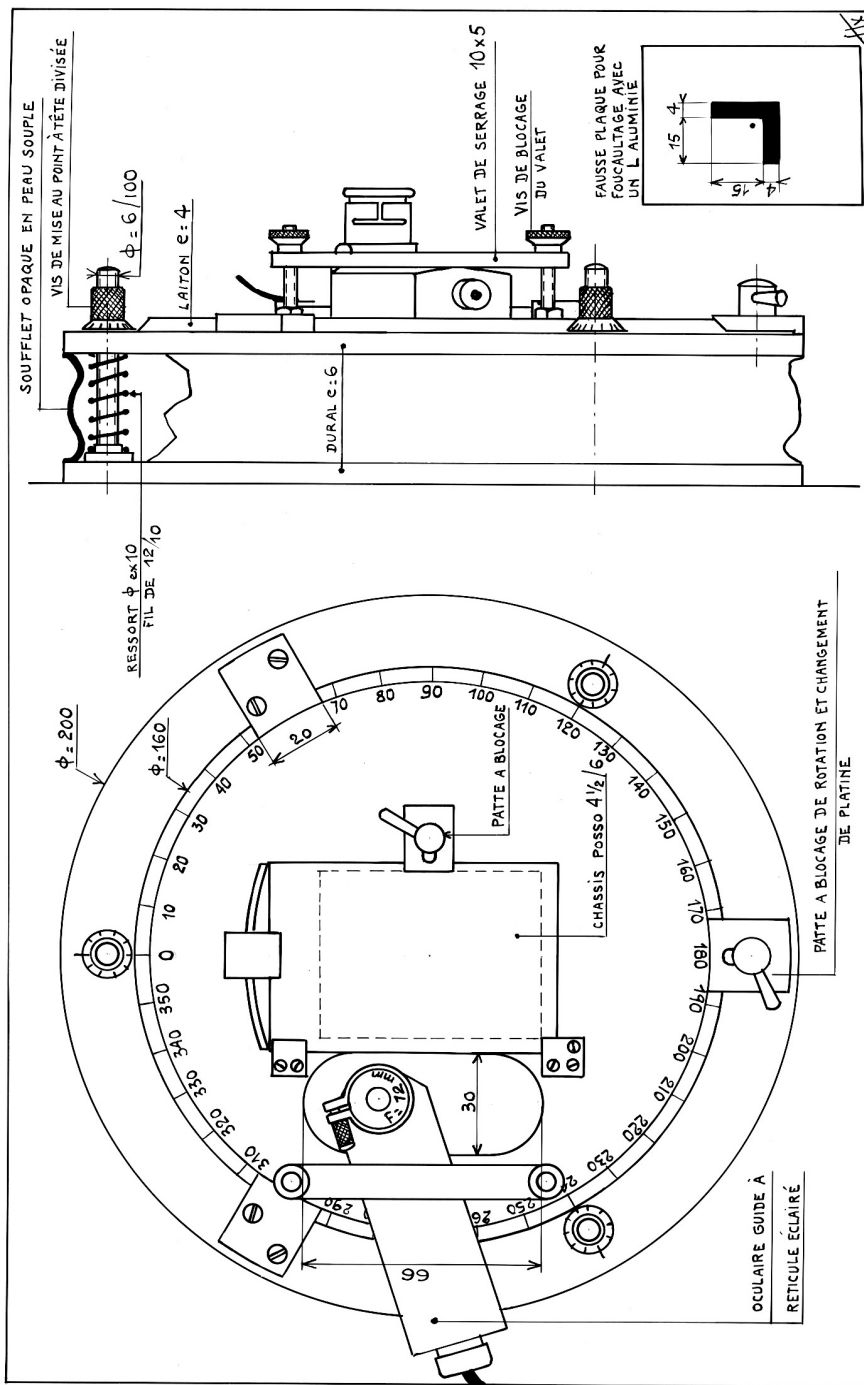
Porte-plaque à oculaire-guide latéral.
